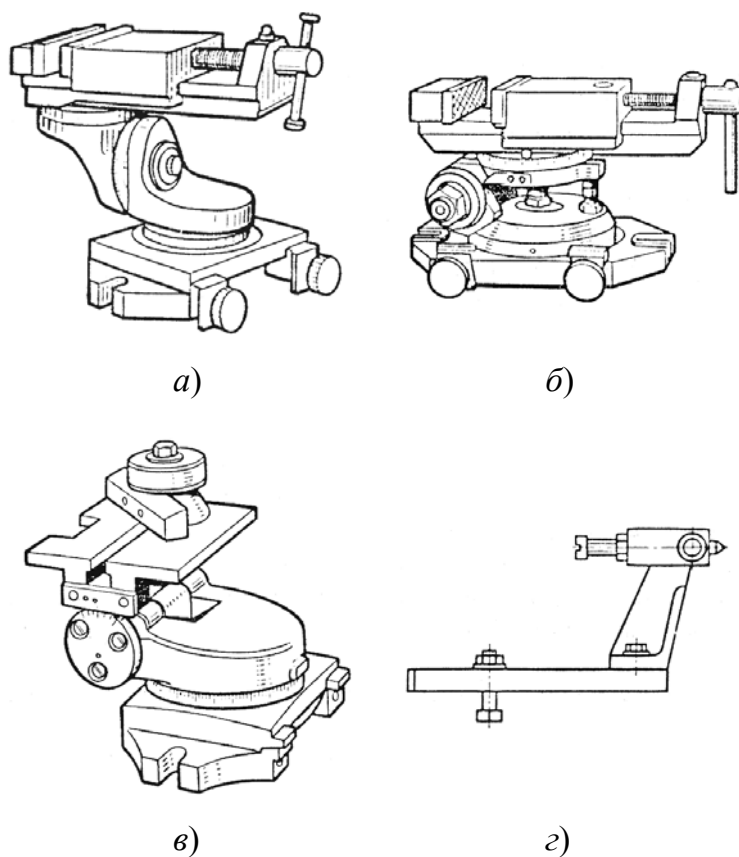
Эскизы приспособлений для заточки инструментов:
